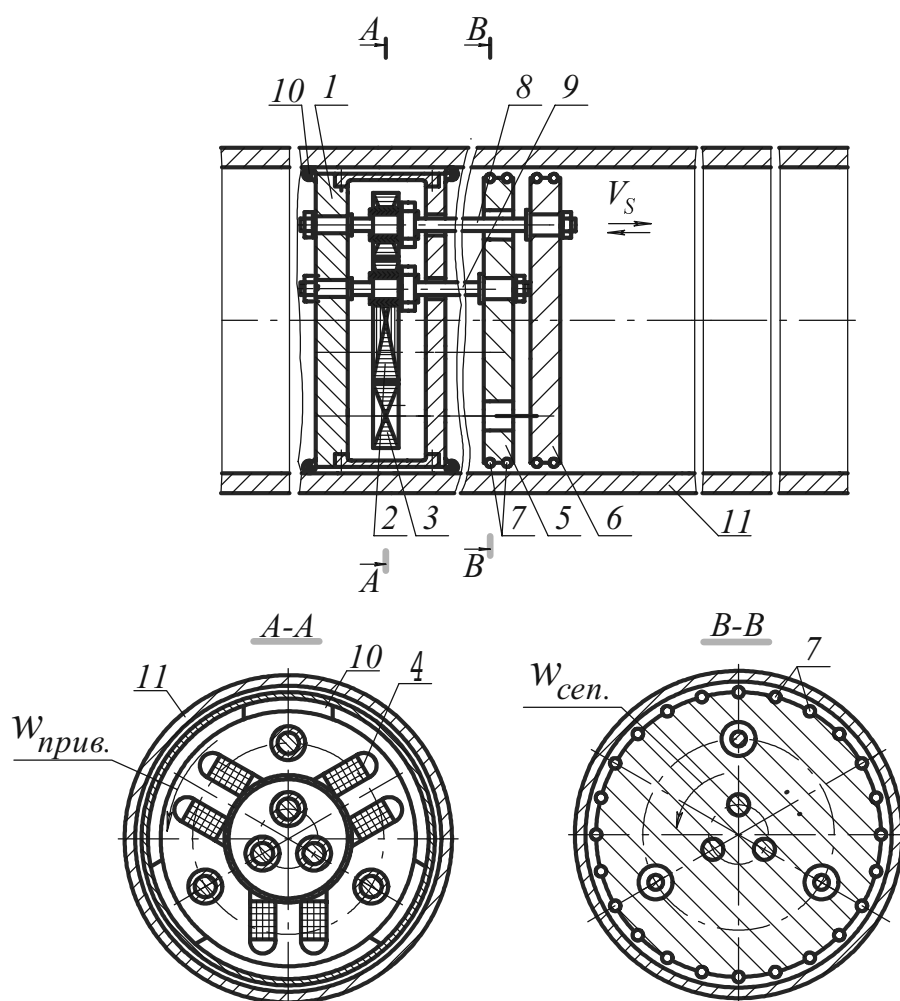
Принципова схема лабораторного однопривідного електромагнітного вібраційного пристрою з пружними системами МТ-1
